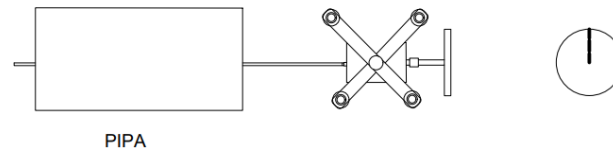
Rancangan Alat Jig & Fixture dalam Explode View
